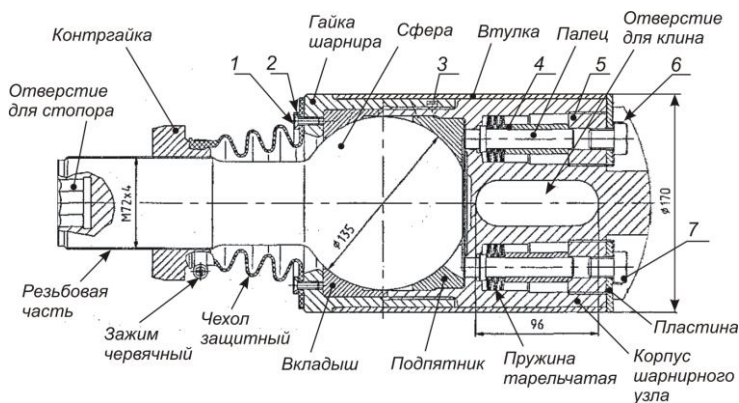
Шарнирный узел для БСУ-3 с разъемным корпусом сцепки:
